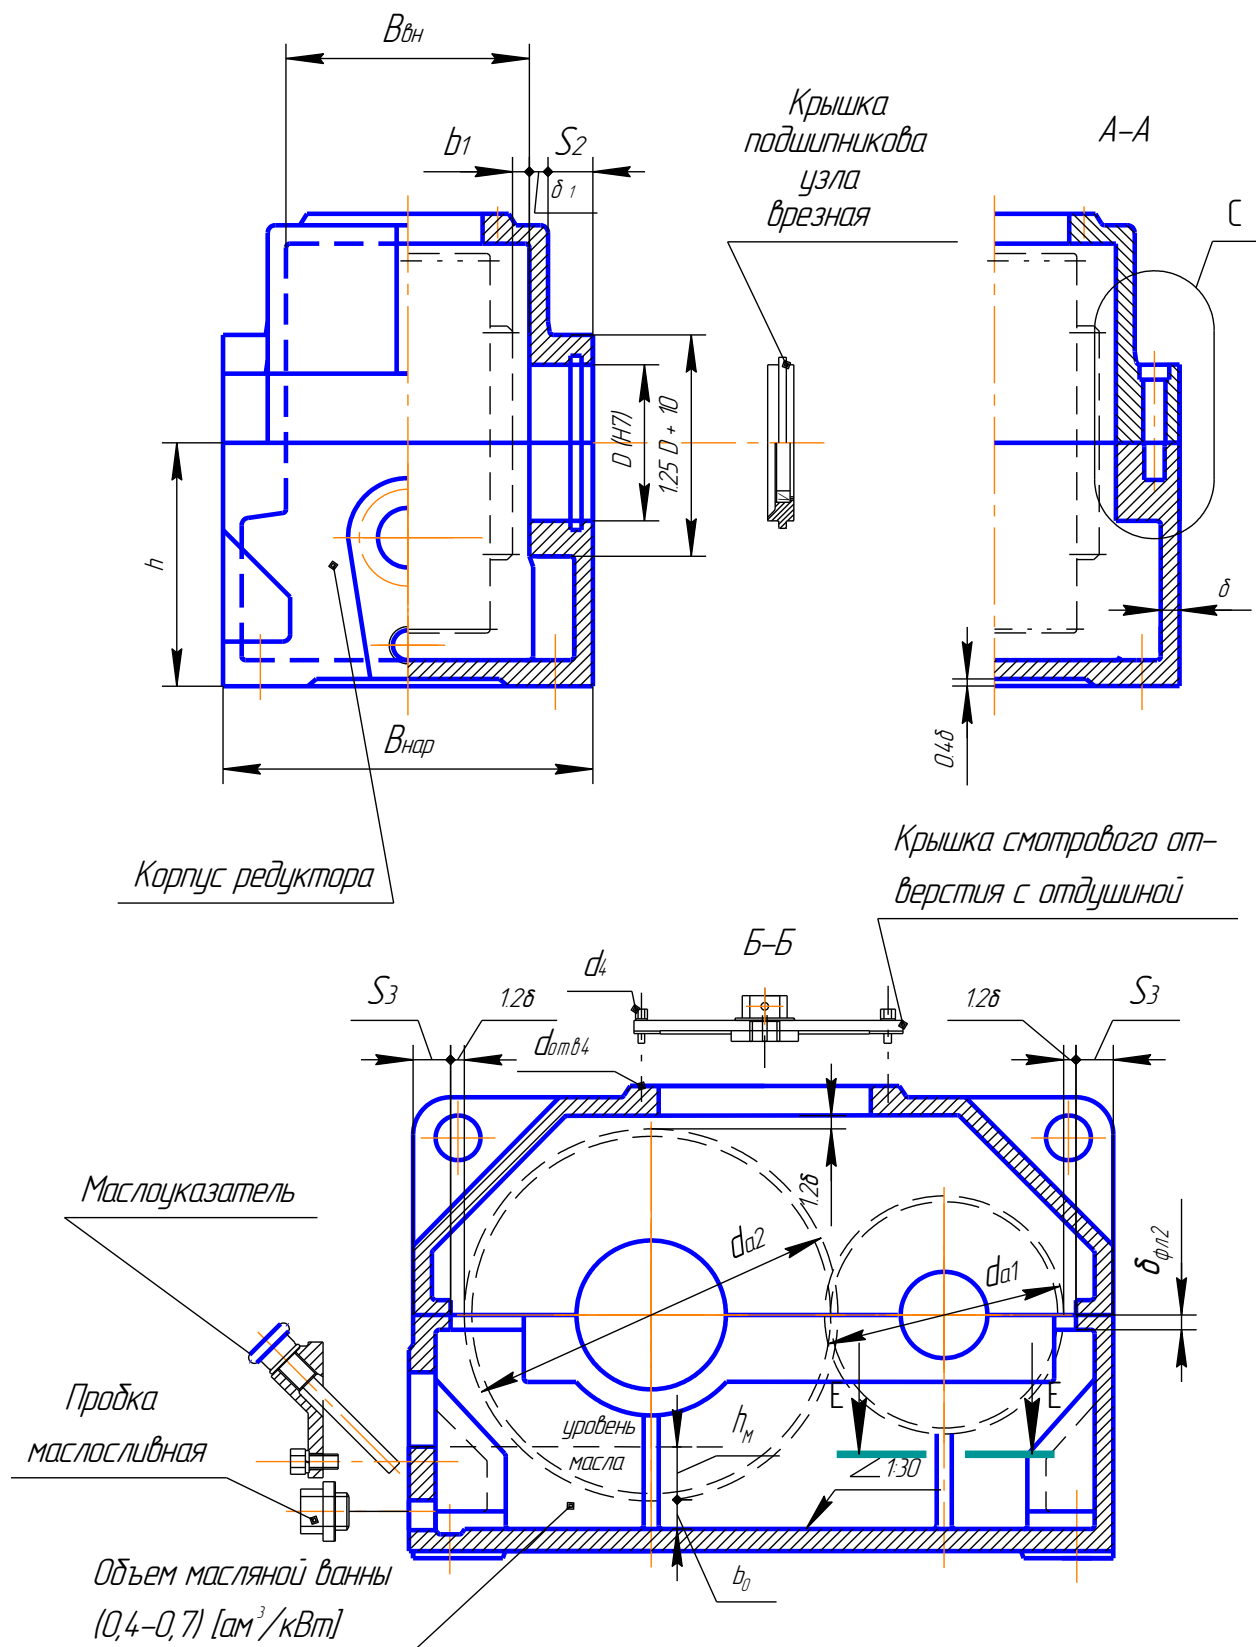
(лист 2, листов 3) Конструкции корпусных деталей цилиндрических редукторов с внутренним расположением подшипниковых бобышек
